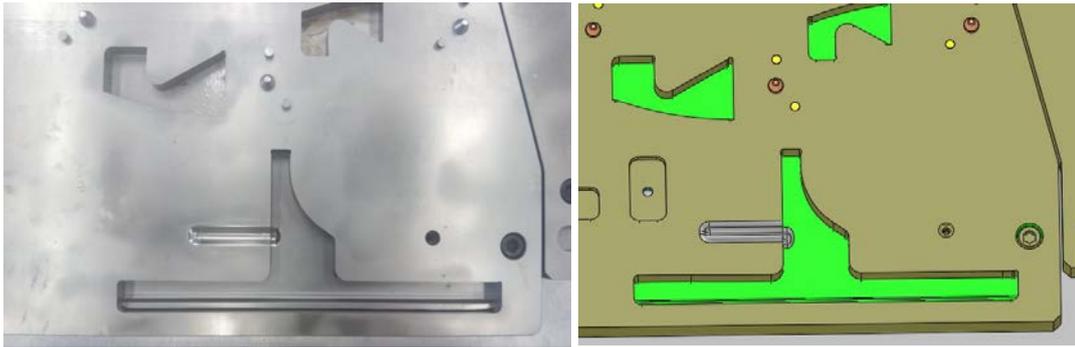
Detalle montaje del punzón de corte exterior y el pisador
